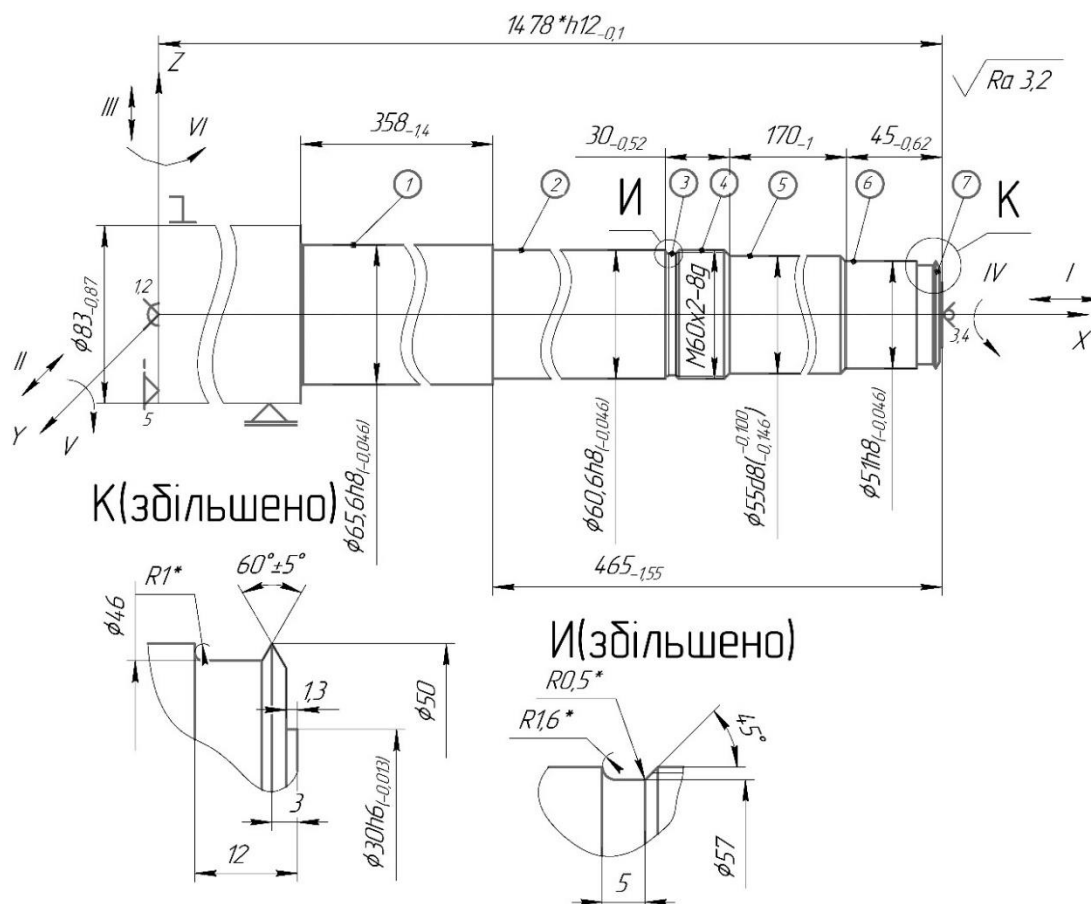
Схема базування заготовки на першому установі для операції 025 токарна.
